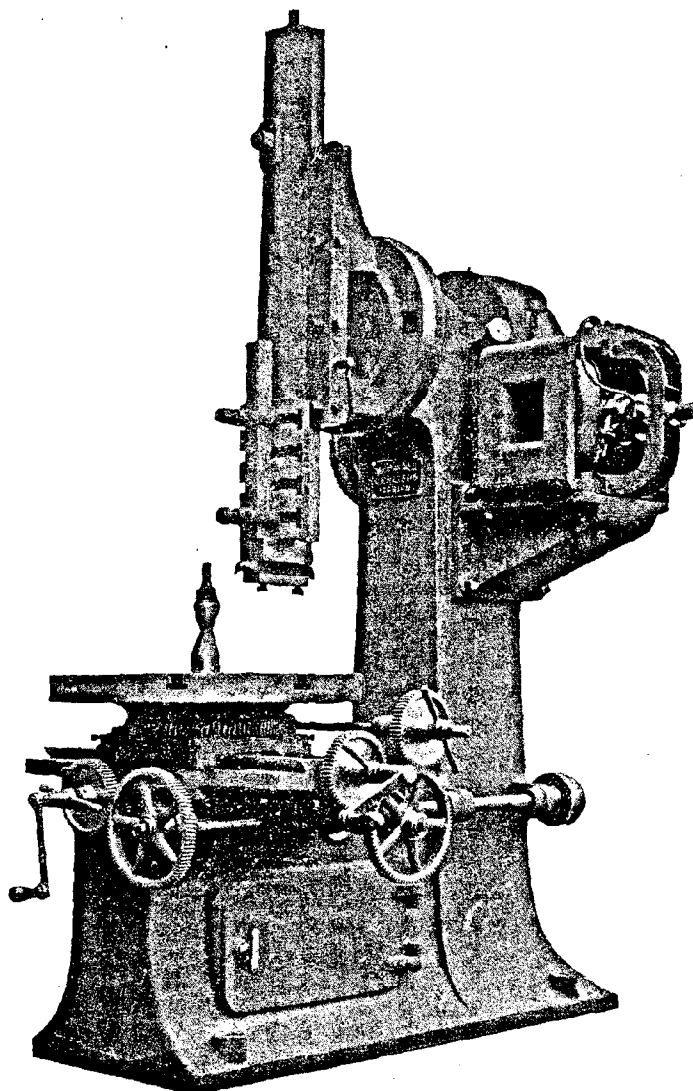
Machine à mortaiser des Ateliers d'Oerlikon.
